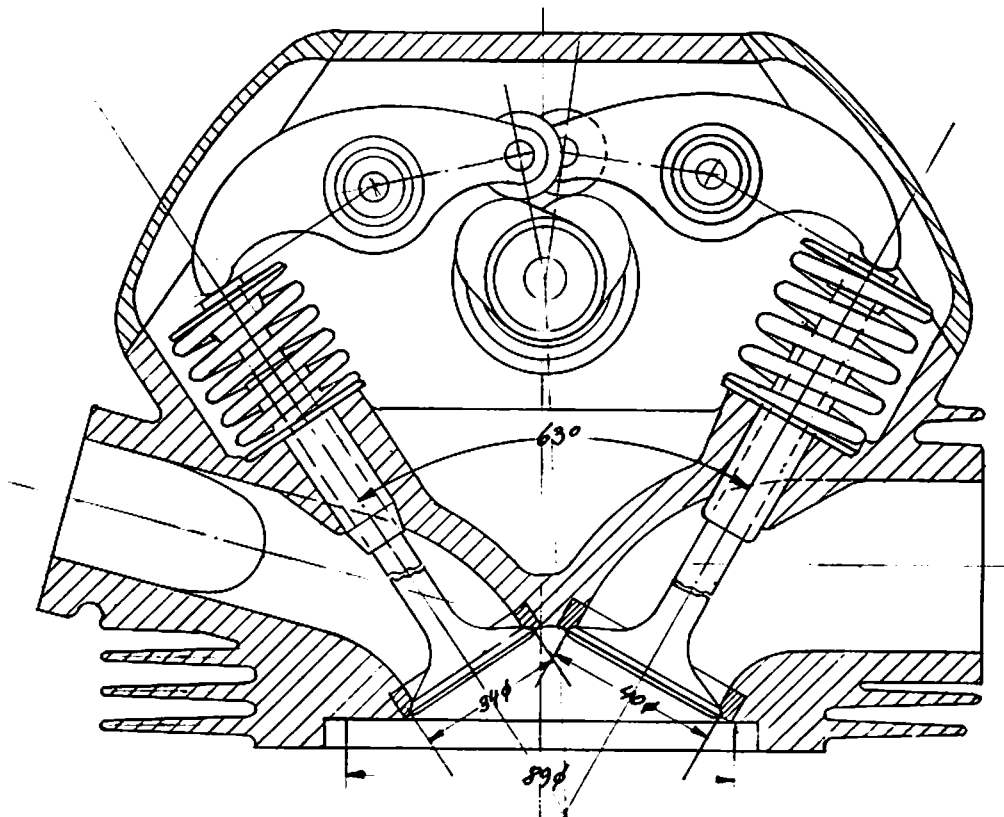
Dreiventilger Dachkopf mit zwei Einlaßventilen.
